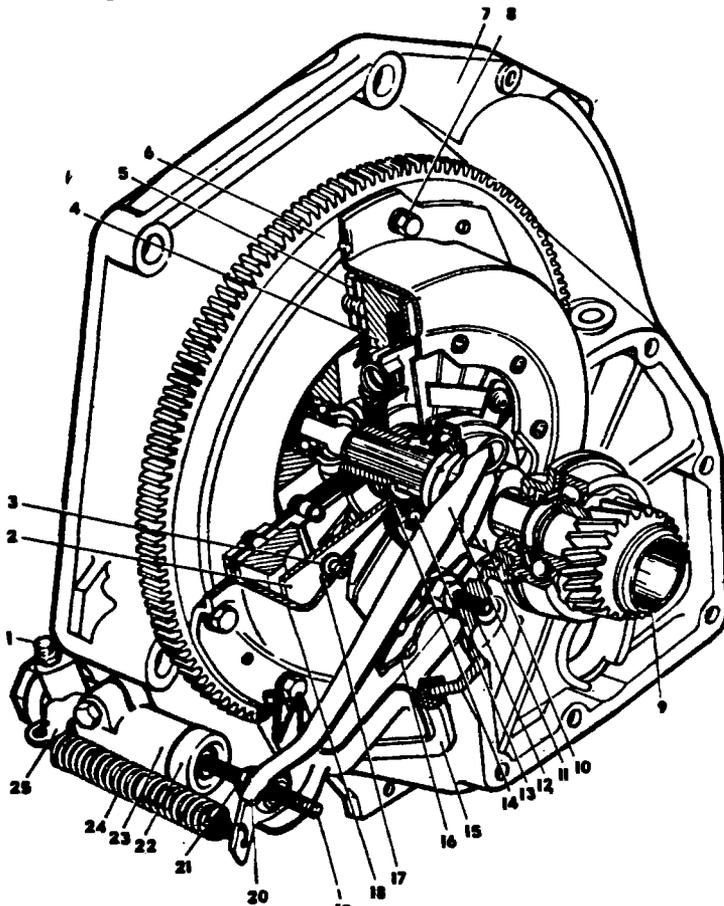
Сцепление в сборе: 1 - штуцер для прокачки; 2 - нажимная пружина сцепления; 3 - ступенчатая заклепка нажимной пружины; 4 - нажимный диск; 5 - ведомый диск; 6 - маховик; 7 - картер сцепления; 8 - болт крепления кожуха сцепления к маховику; 9 - первичный вал коробки передач; 10 - муфта подшипника выключения сцепления; 11 - вилка выключения сцепления; 12 - шаровая опора вилки выключения сцепления; 13 - подшипник выключения сцепления; 14 - упорный фланец нажимной пружины; 15 - чехол вилки выключения сцепления; 16 - пружина вилки выключения сцепления; 17 - опорное кольцо нажимной пружины; 18 - кожух сцепления; 19 - толкатель вилки выключения сцепления; 20 - регулировочная гайка; 21 - контргайка; 22 - защитный колпачок цилиндра привода выключения сцепления (рабочий цилиндр); 23 - цилиндр привода выключения сцепления (рабочий цилиндр); 24 - оттяжная пружина вилки; 25 - скоба оттяжной пружины
